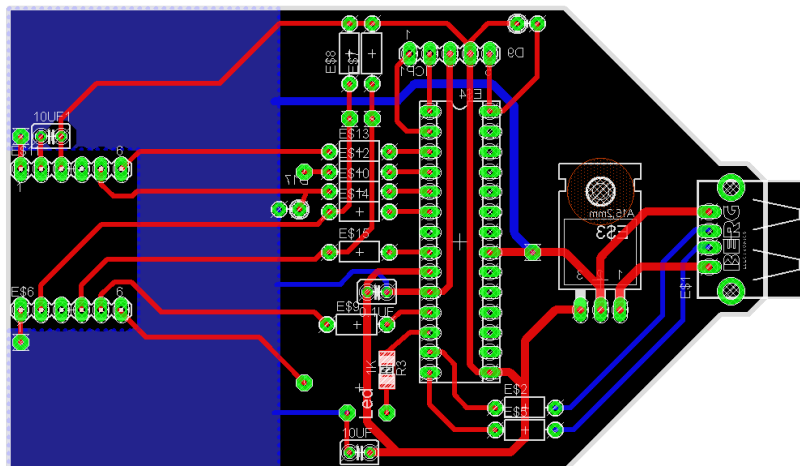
Diseño en Eagle de la tarjeta de circuito impreso para el nodo principal.
